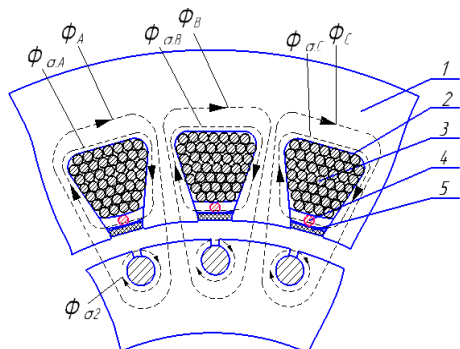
Расположение измерительной обмотки преобразователя тока в напряжение в пазах статора асинхронного двигателя и вид магнитных потоков: 1- магнитный сердечник статора, 2-пазы статора, 3- основная обмотка статора, 4-измерительная обмотка, 5- клинья пазов
